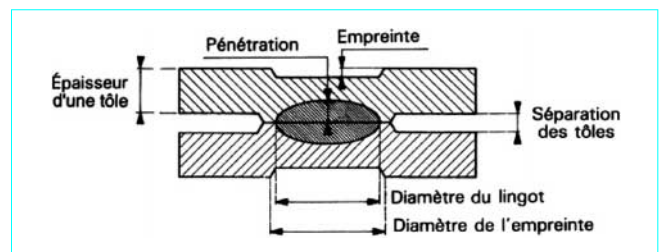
Soudage par points : caractéristiques dimensionnelles d'un point de soudure
